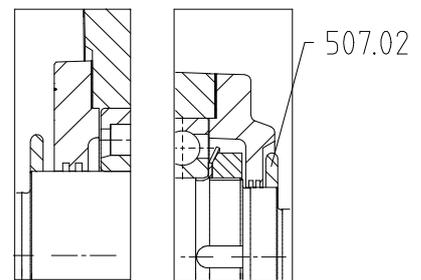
Сборочный чертеж стандартного исполнения (с жидкой смазкой)
